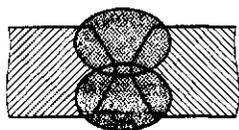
Стыковое соединение с двумя симметричными скосами кромок
